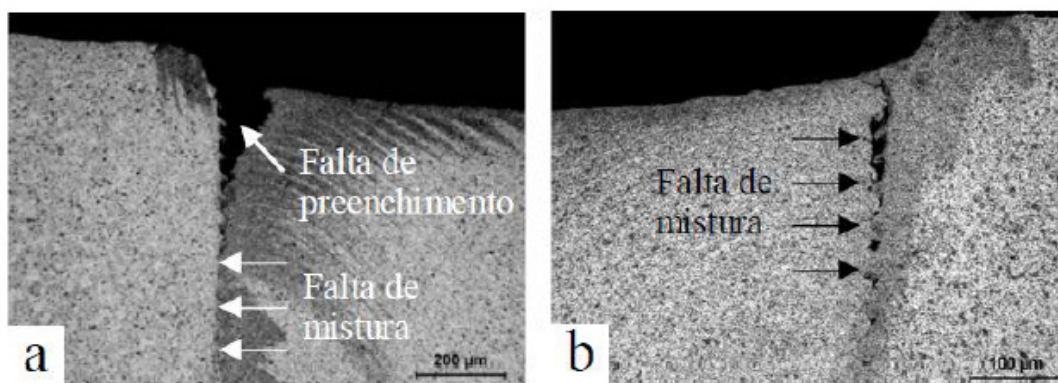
Defeitos volumétricos dentro da zona de mistura da junta de alumínio AA2023 cladeado soldada por *FSpW* [52].
